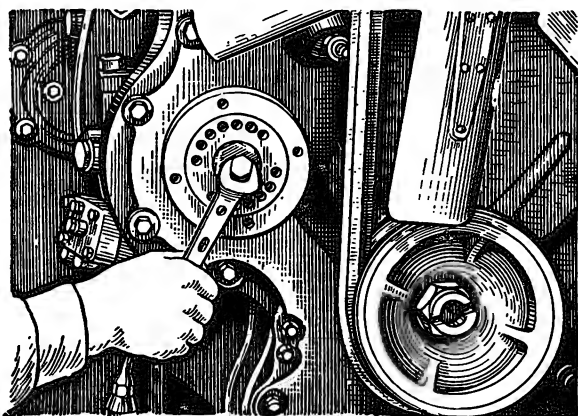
Регулировка угла начала подачи топлива путем изменения положения шлицевой шайбы относительно шестерни привода
